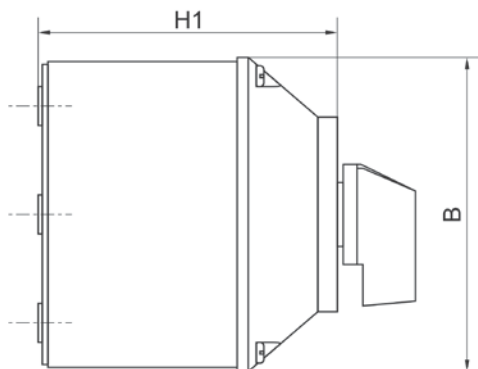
Габаритные размеры переключателя закрытого исполнения – РК.
